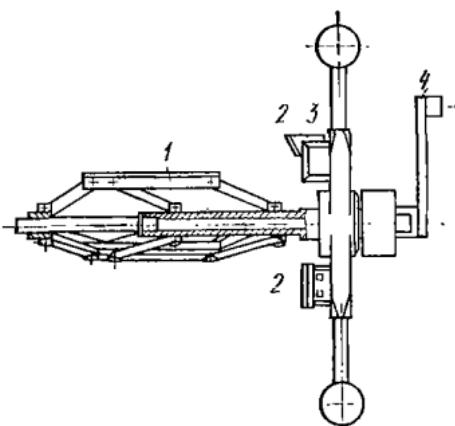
Устройство для торцовки и снятия фасок на концах пластмассовых труб:
